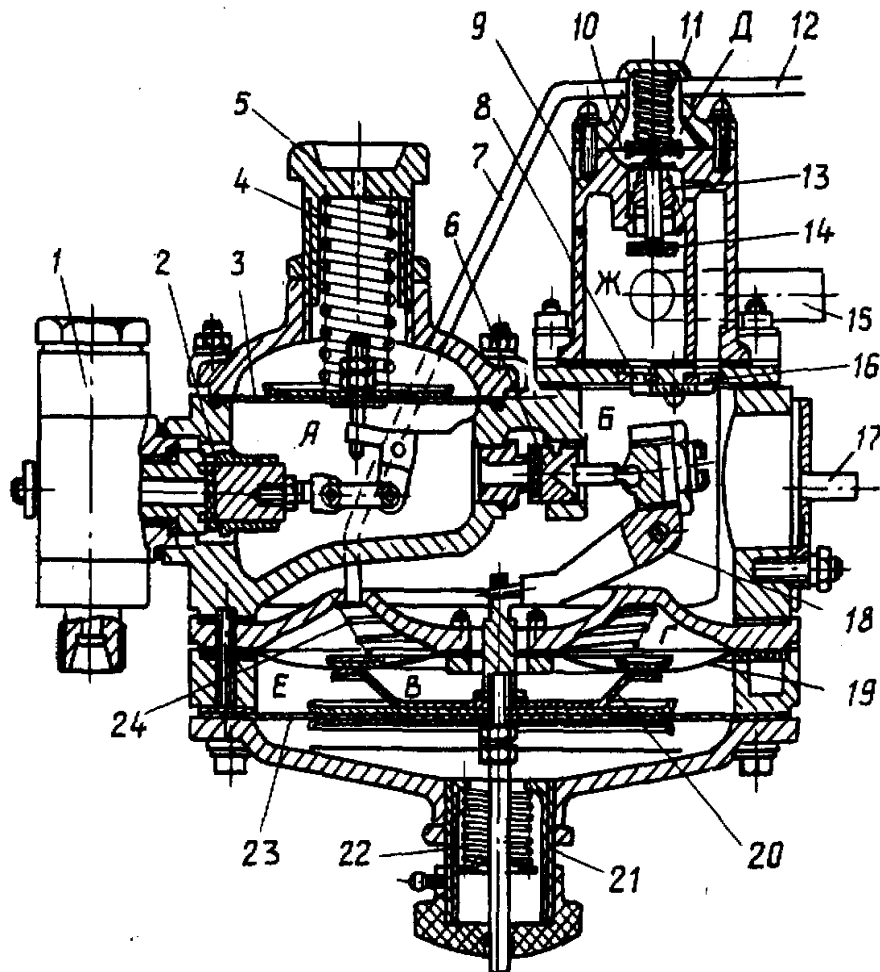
Схема двоступеневого редуктора для газових двигунів
